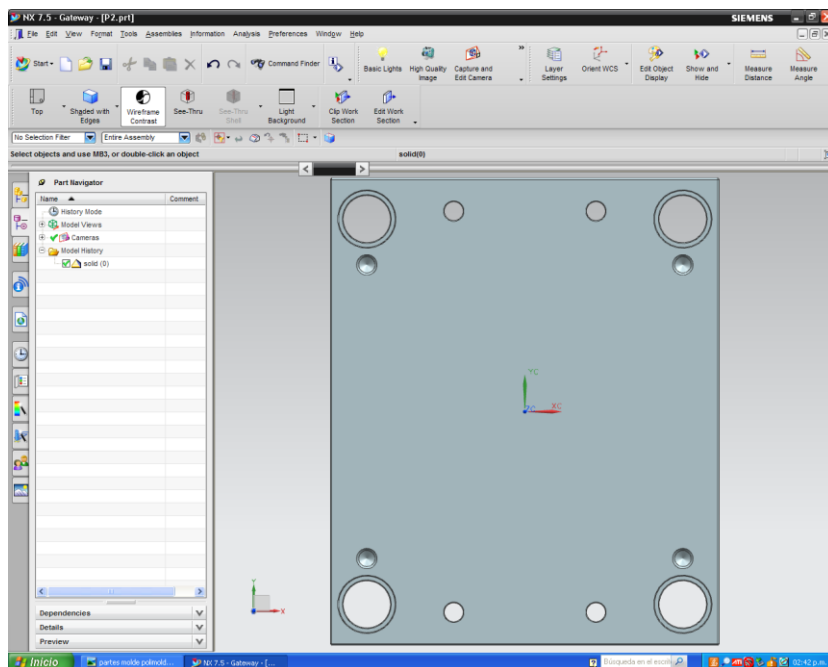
Placa posterior de cavidad P2, vista frontal.
